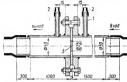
Приспособление для замеров расхода воздуха и газа: I — ниппеля для подсоединения дифманометра; 2 резиновые тоубки для подключения: 3 — диафовгма.
